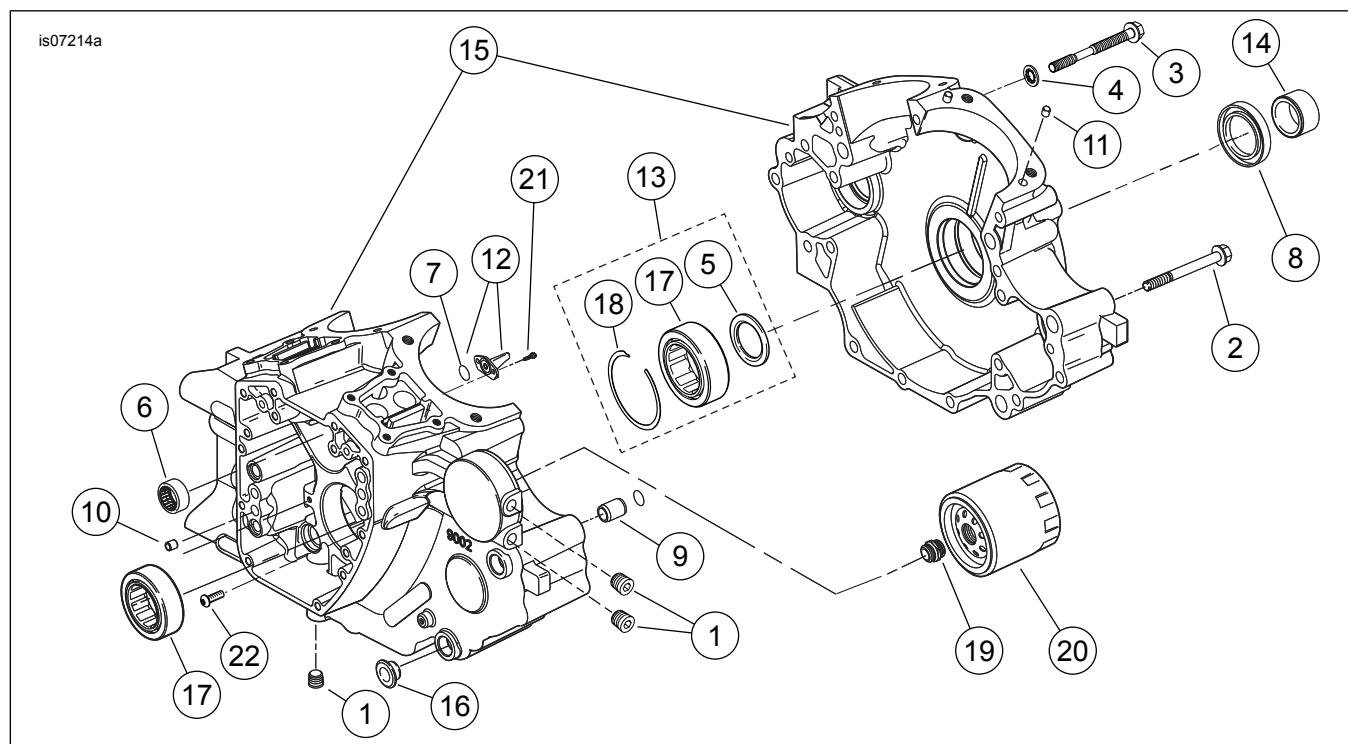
SE120R Screamin' Eagle Pro Crate Engine (Beta) Cáster, filtro de aceite del motor y refrigerador
